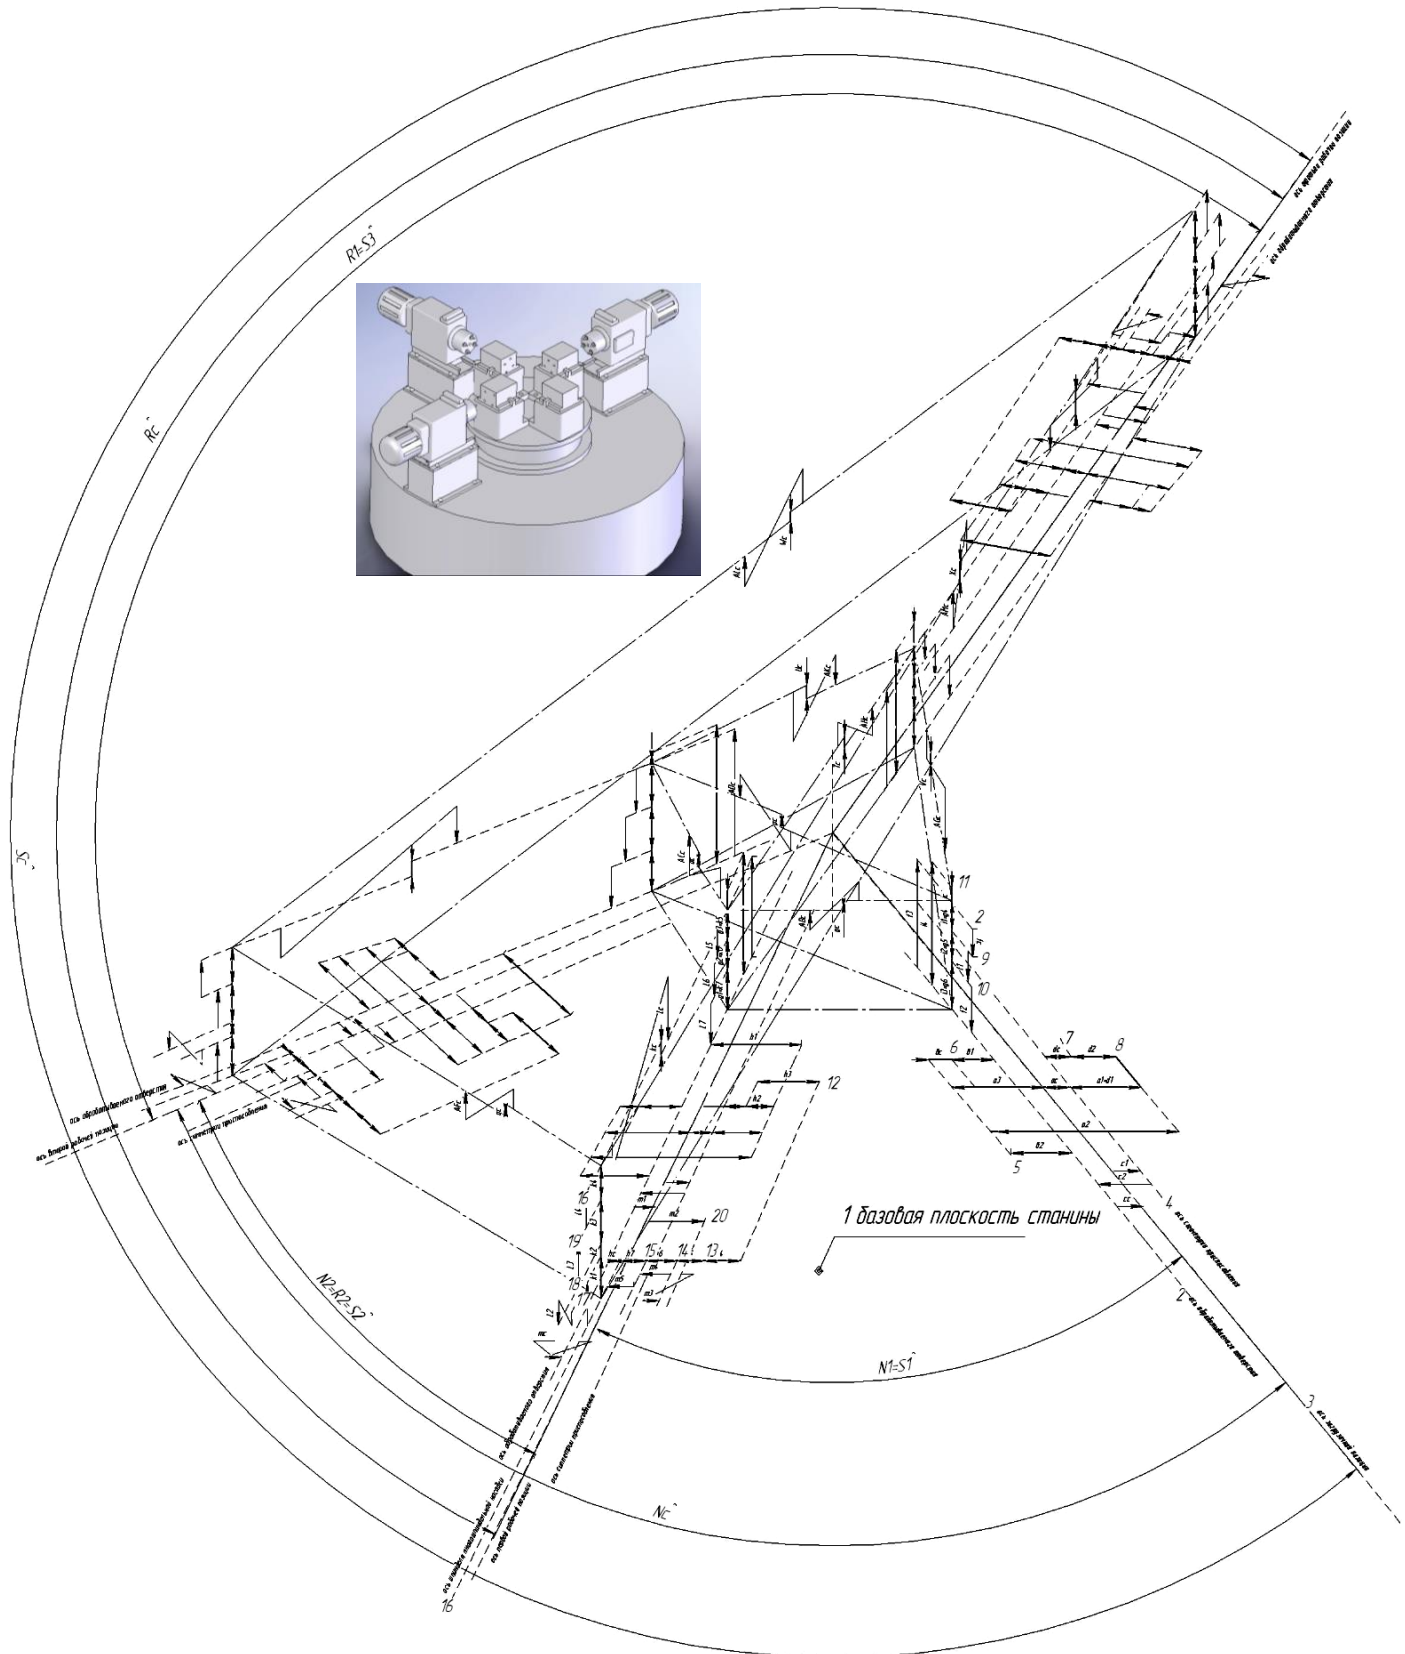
Тривимірний модель багатопозиційного агрегатного верстата і просторові розмірні ланцюги до неї
